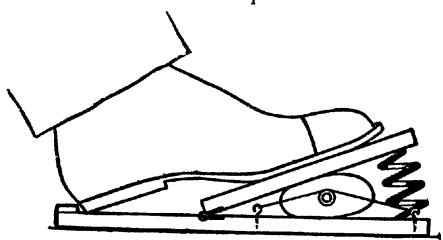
Станок ножной для каучуковой груши (вид сбоку).
